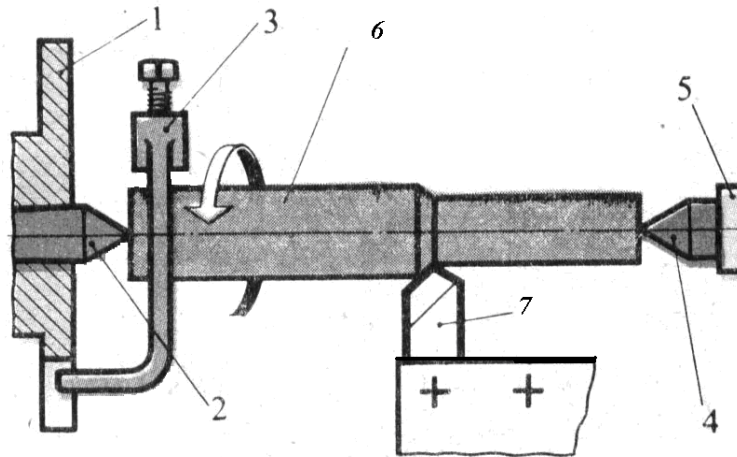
Заготовка, що встановлена в центрах: 1 – планшайба, 2 – передній центр, 3 – хомутик, 4 – задній центр, 5 – піноль, 6 – заготовка, 7 - різець
